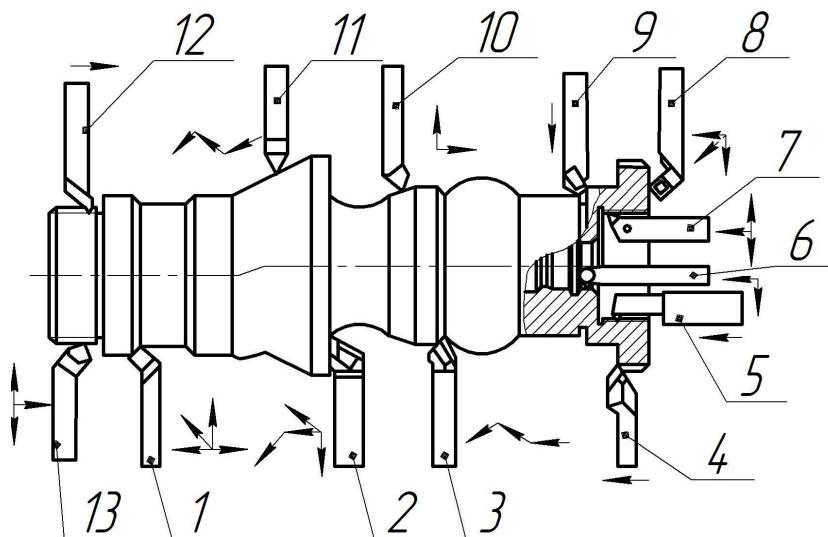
Схеми обробки токарними різцями основних типових поверхонь: 1, 8 – прохідними з квадратними ЗБП; 2 – контурним з ромбічною ЗБП; 3, 10, 11, 13 – контурними з трикутними ЗБП; 4, 12 – різьбовими для нарізання зовнішніх різьб; 5 – різьбовим для нарізання внутрішніх різьб; 6, 7 – розточувальними з ромбічною та трикутною пластинами; 9 – для проточування канавок
